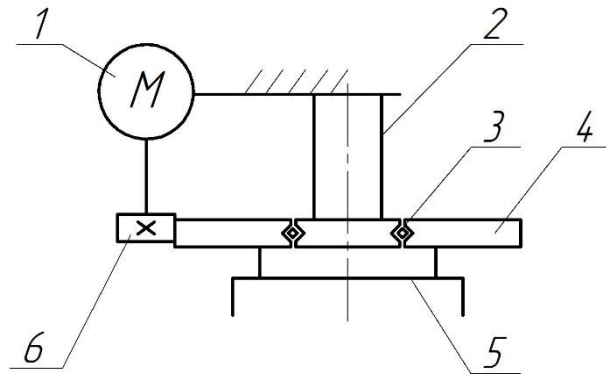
Кінематична схема механізму повороту спредера: 1 – мотор; 2 – рама перехідна; 3 – вузол опорний підшипниковий; 4 – вінець зубчастий; 5 – рама верхня (поворотна частина спредера); 6 – шестірня
